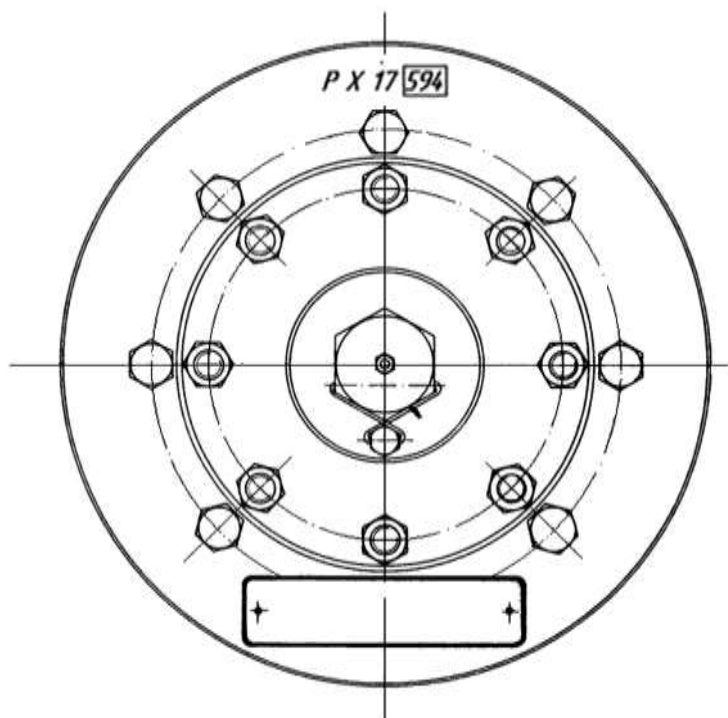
Маркировка на торце кожуха упругой муфты
